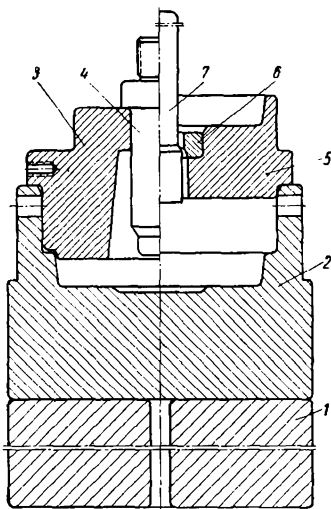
Общий вид штампа для второй операции штамповки ступицы: 1 — подставка; 2 — нижняя часть штампа; 3 — верхняя часть штампа; 4 — прошивной пуансон; 5 — матрица для пробивки; 6 — кольцо; 7 — пуансон для пробивки
